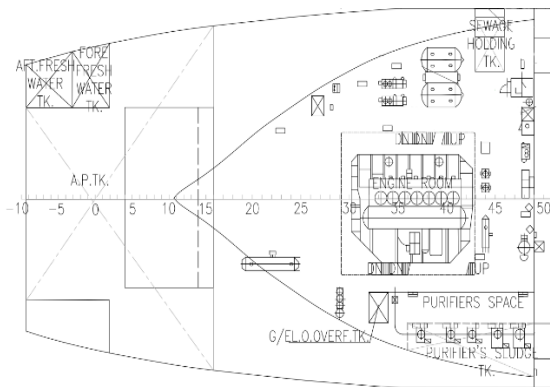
Floor Level - Engine Room dengan Penambahan BWTS
